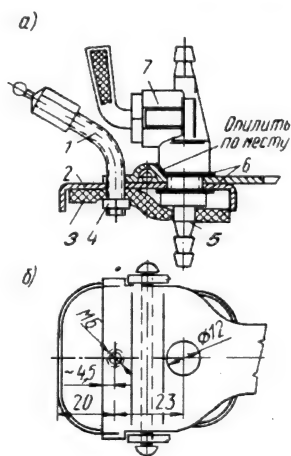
Сборка краника и воздушной трубки на крышке канистры
